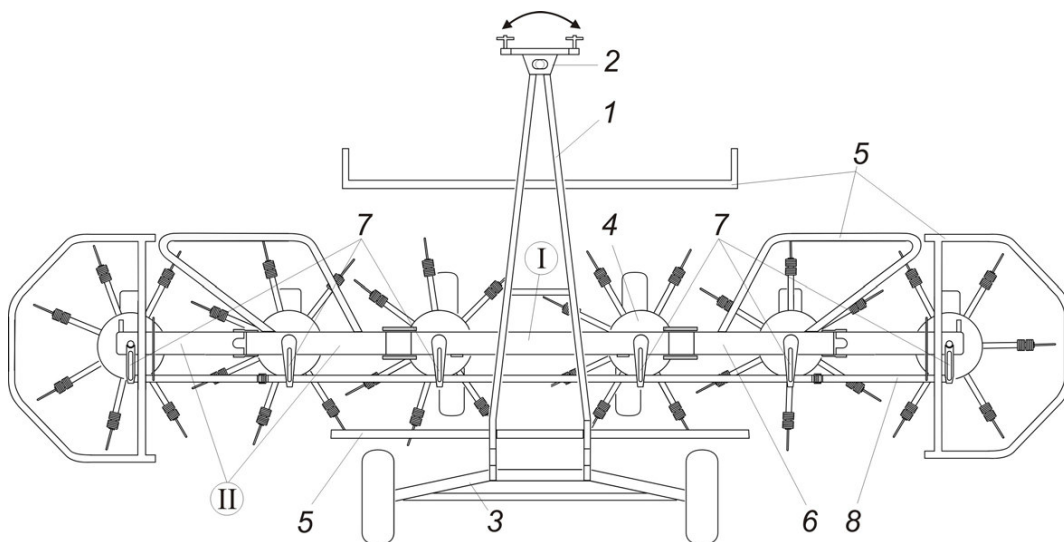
Схема ворошителя-вспушивателя роторного ВВР-7,5 в рабочем положении:
